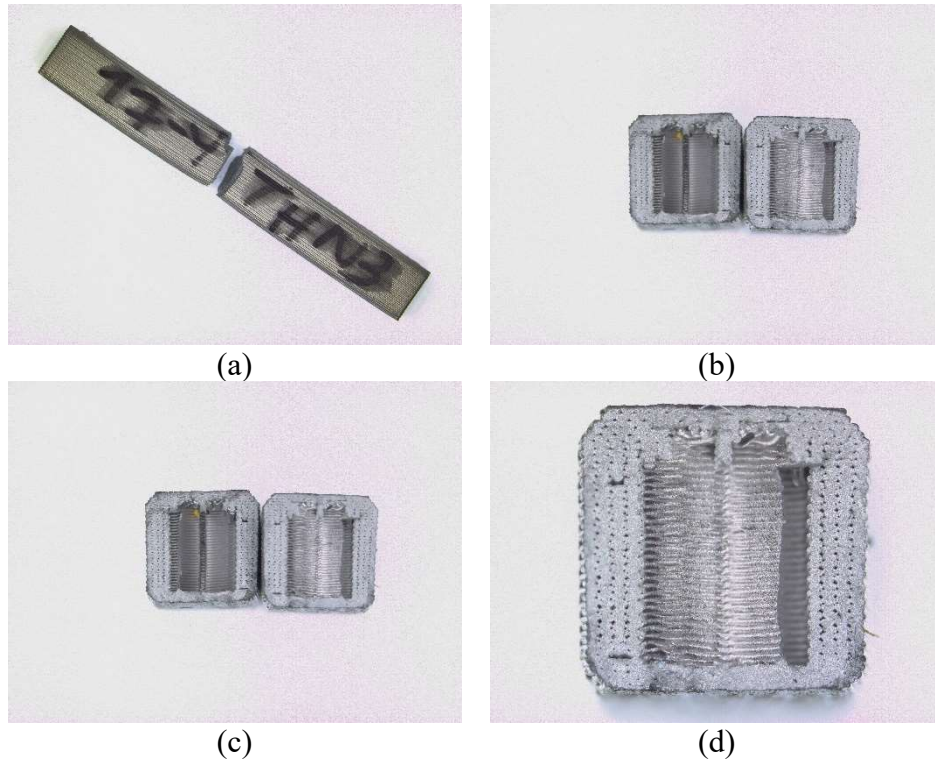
Resultado del ensayo de flexión de la probeta con la configuración 17-4THN, a) Vista superior de la probeta tras la fractura. b) Vista frontal, enfoque en la mitad izquierda. c) Vista frontal, enfoque en la mitad derecha. d) Vista detallada del interior, mostrando la estructura de relleno (Elaboración propia).
